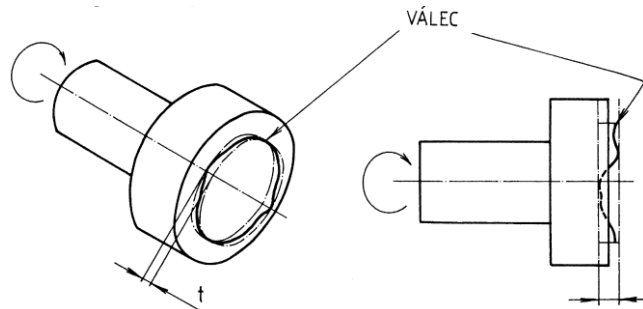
Vyobrazení tolerančního pole obvodového kruhového házení [3]
